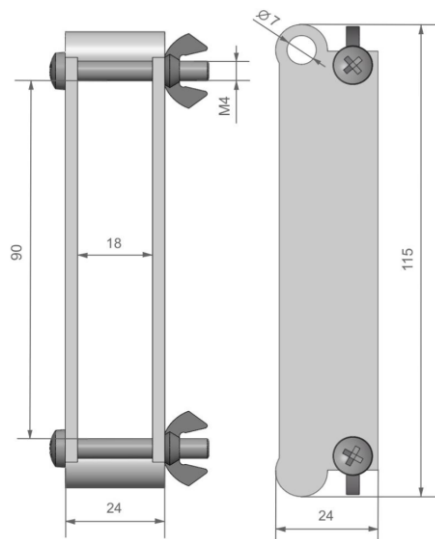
Dimensiones pieza para el ensayo de flexión en configuración de voladizo 3 || Fuente: Elaboración propia
